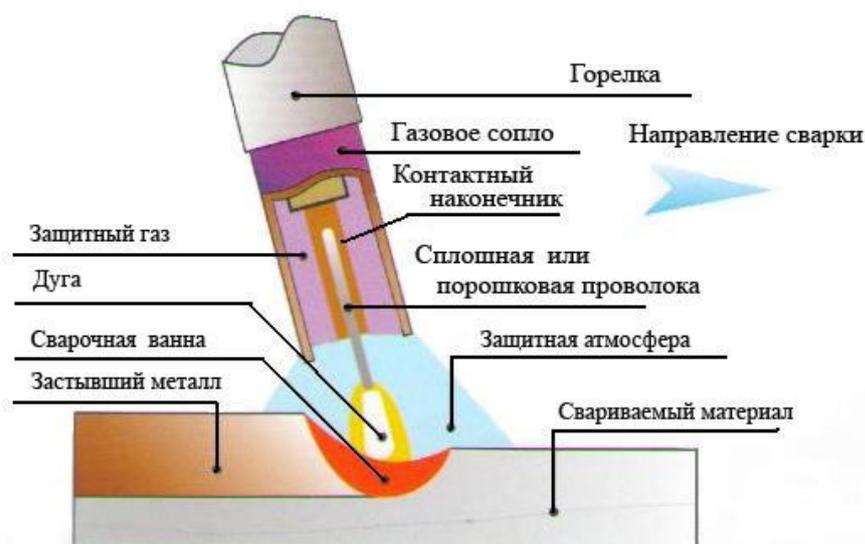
Схема процесса механизированной дуговой сварки самозащитной порошковой проволокой
